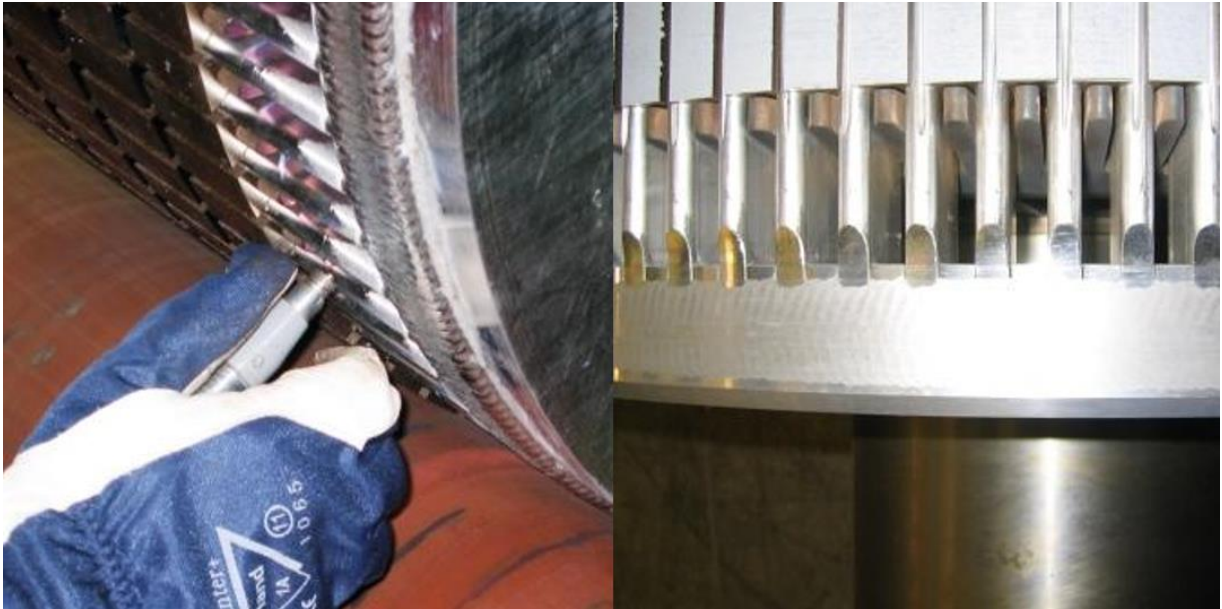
Сварочный процесс завершен, механическая обработка завершена
